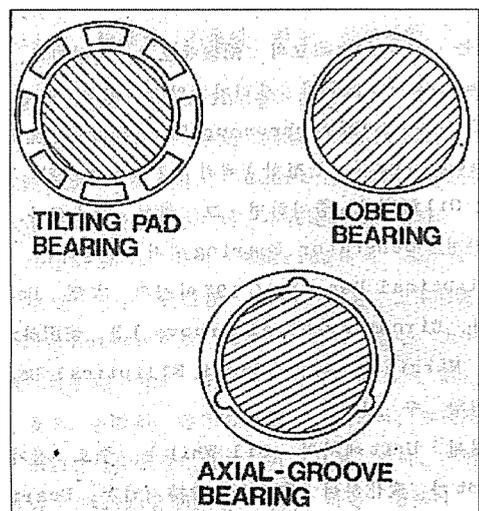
Oil Whip의 생성방지를 위한 특수 Bearing
